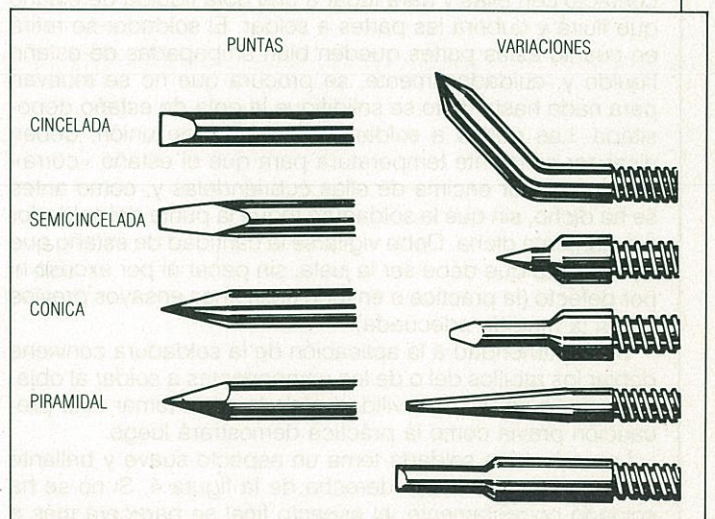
Diversas formas y variantes de punta de soldador.
